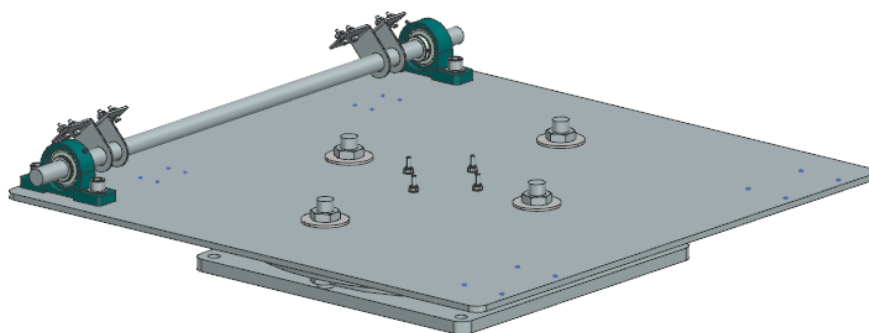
Piezas 'Apoyo centro' y 'Guía apoyo'.
